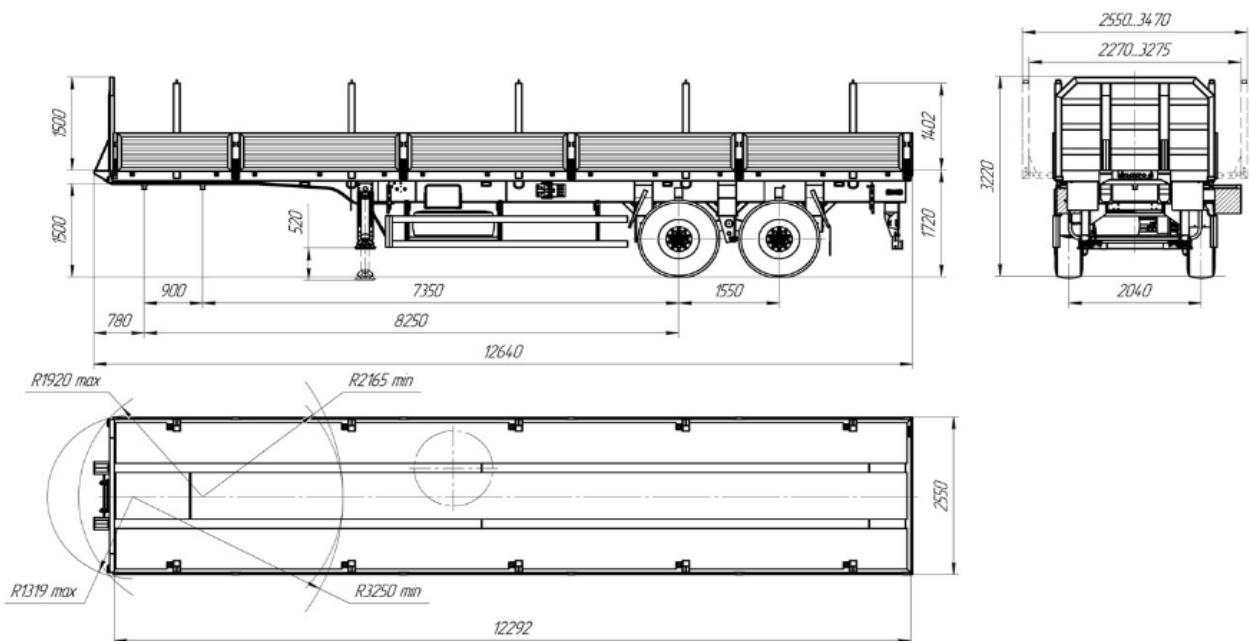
чертеж бортового полуприцепа УЗСТ 9180-09Б2
